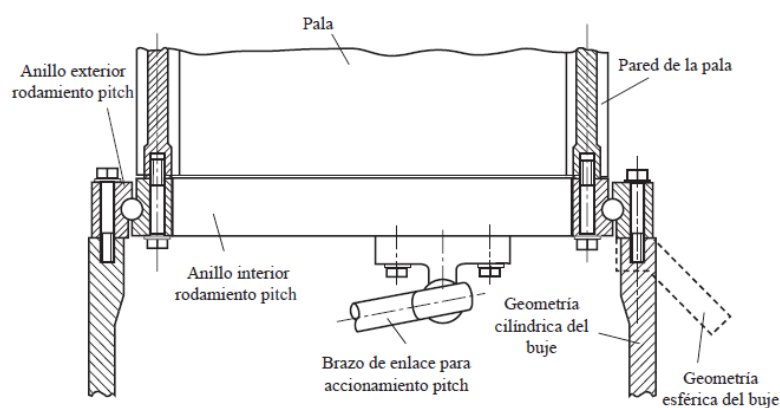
Disposición típica de un rodamiento pitch (Fuente: [21])
